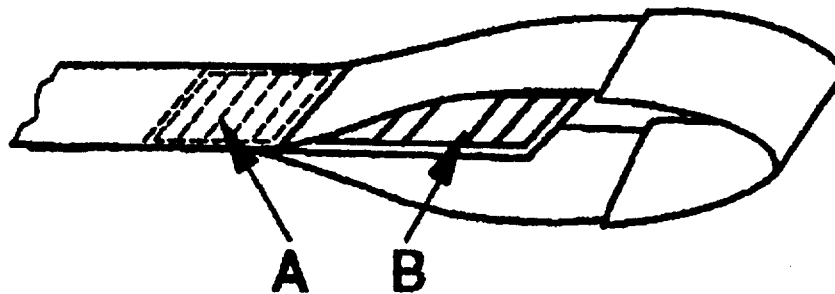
Typische Befestigung des Etiketts an einem Schlaufenhebeband
